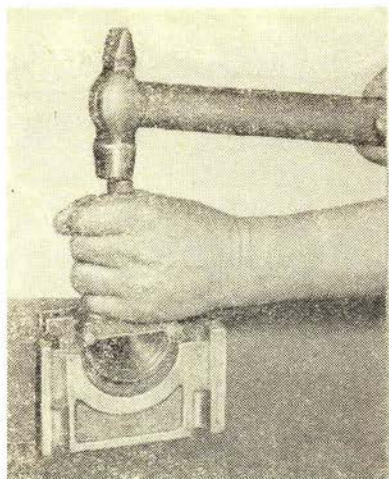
Укладка заднего сальника коленчатого вала в сальникодержатель
